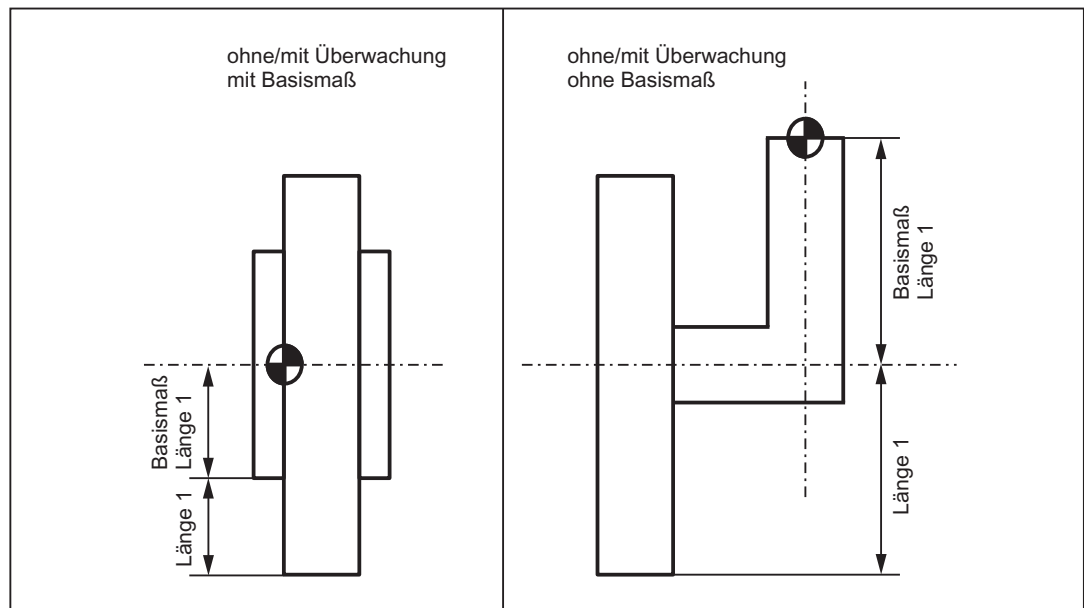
Struktur der Werkzeugkorrekturdaten bei Schleifwerkzeugen
